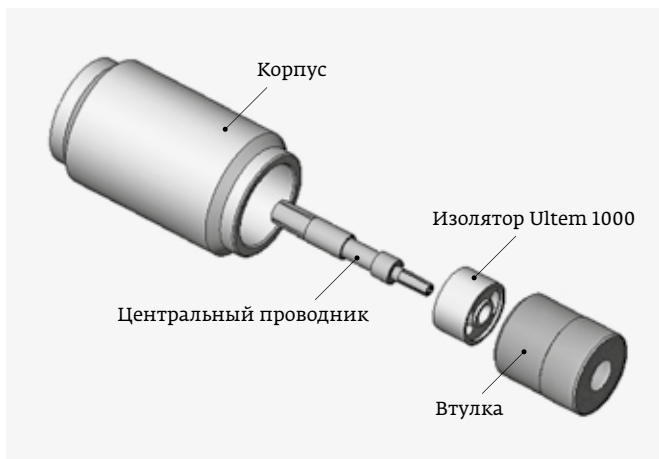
Схематическое изображение конструкции соединителя 2.92 mm компании Radiall
